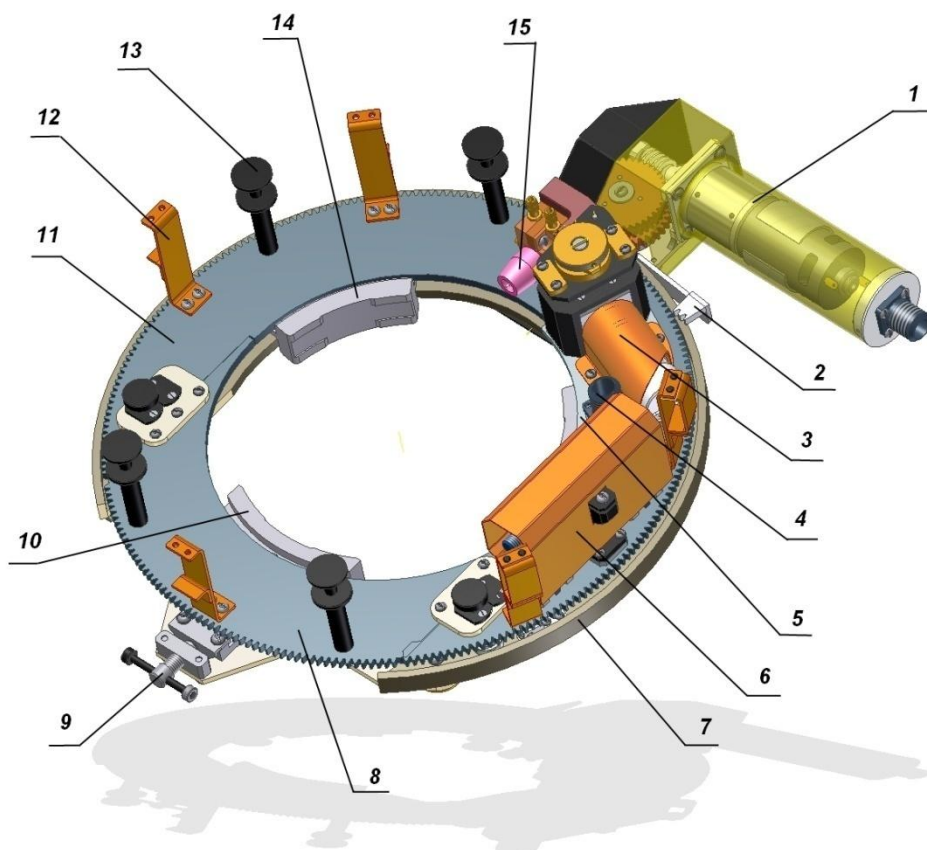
Конструкция сварочной головки ГНС 220
